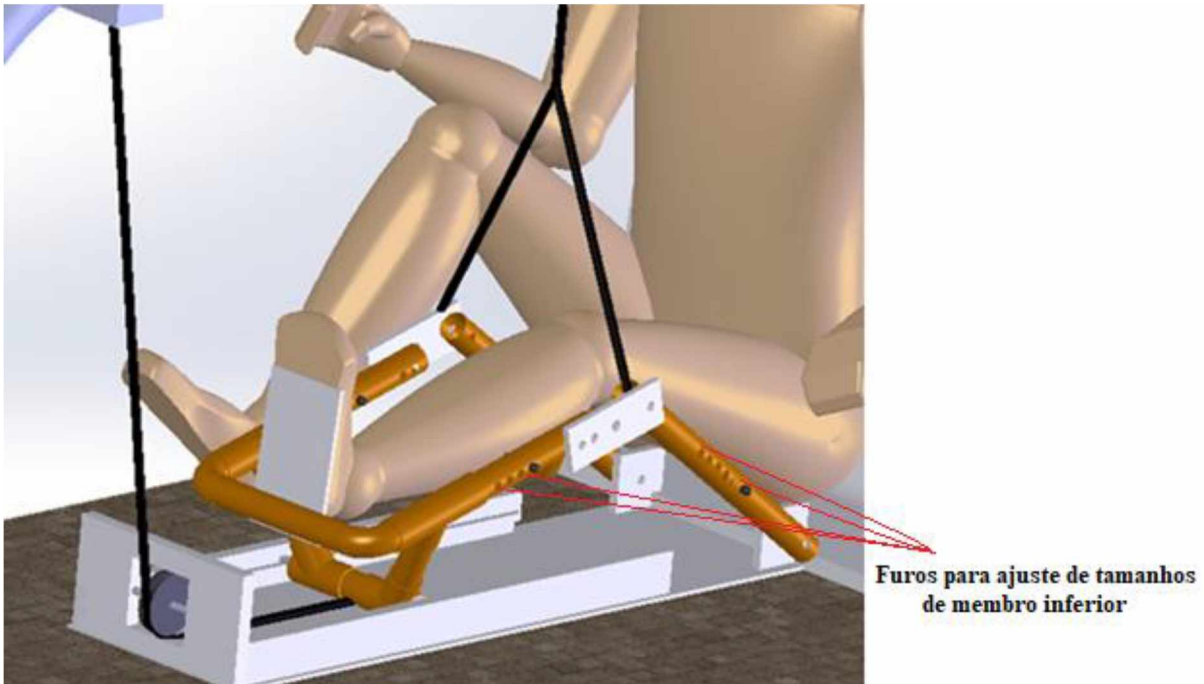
Dispositivo proposto modificado, visto por outro ângulo.
